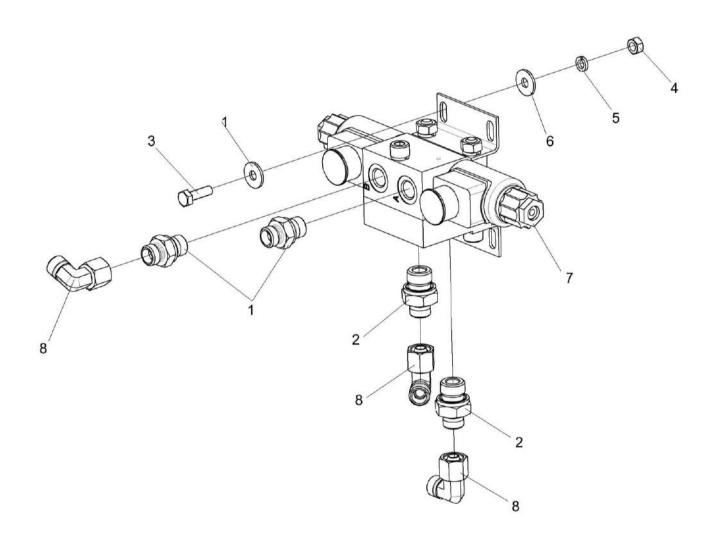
Гидроблок доворота вала мотора ГСТ КВК-2-0601460А
